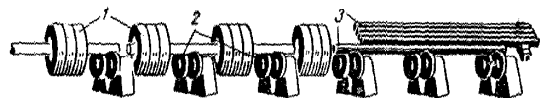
Схема нагревателя с секционированным индуктором и роликовым механизмом для перемещения и вращения заготовок:
